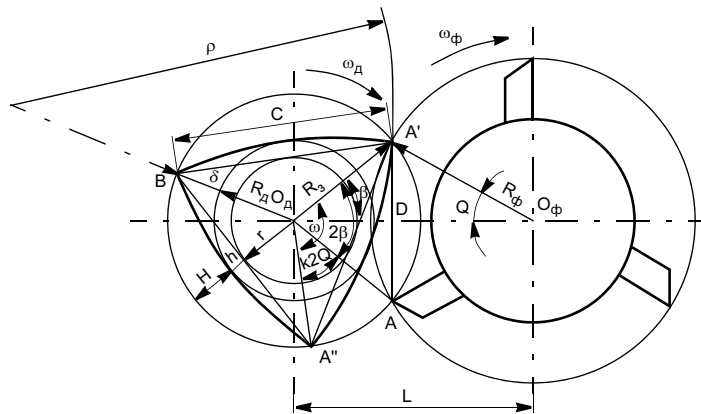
Схема встречного фрезоточения некруглого профиля с внешним касанием детали и фрезы
